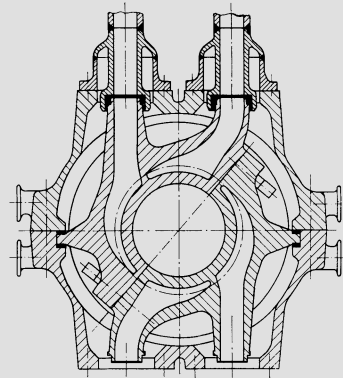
Eingesetztes, frei dehnbares Einströmgehäuse einer Großdampfturbine mit Düsengruppenregelung (BBC); beachte die spiralartige Gestaltung der Düsengruppen-Zuströmkanäle
